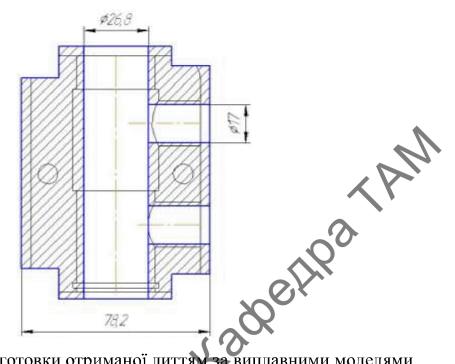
Ескіз заготовки отриманої литтям за виплавними моделями
